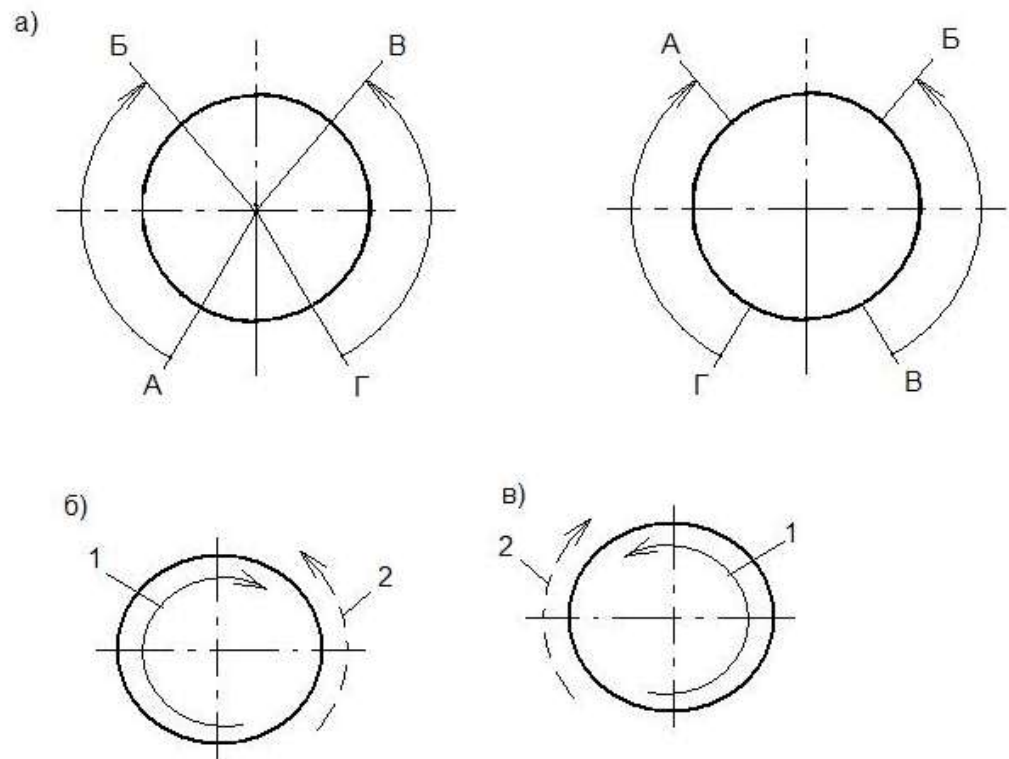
Сварка поворотных стыков газопроводов.
